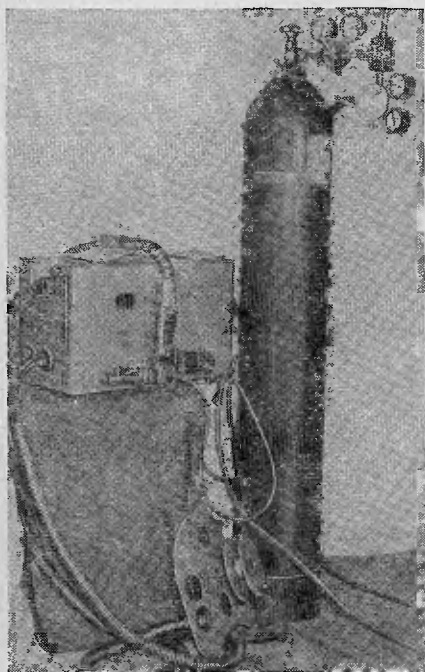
Полуавтоматическая установка для аргонодуговой сварки плавящимся электродом ПШП-9.
